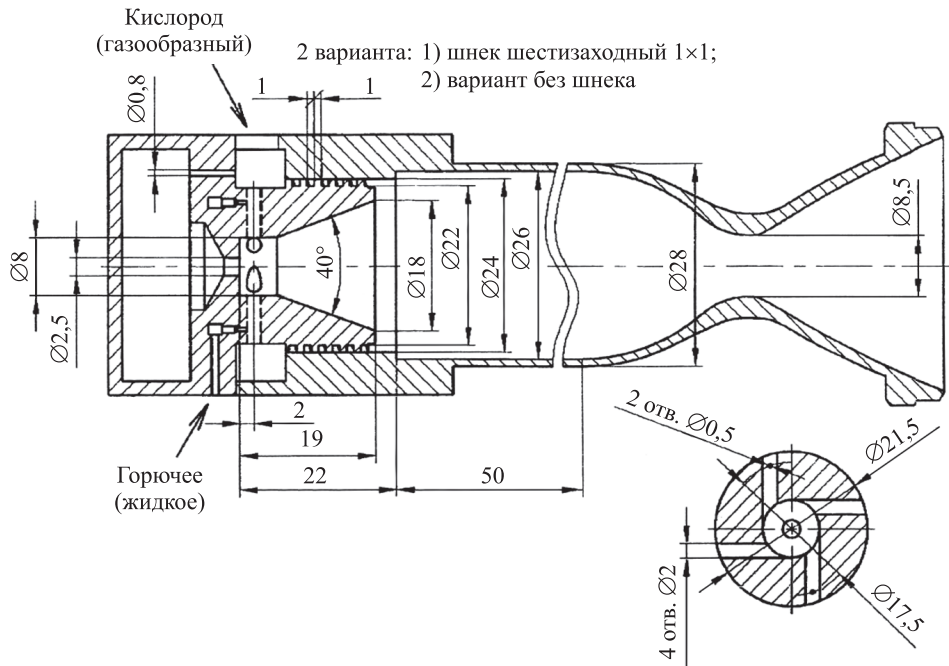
Конструкция рассчитываемой камеры двигателя:
